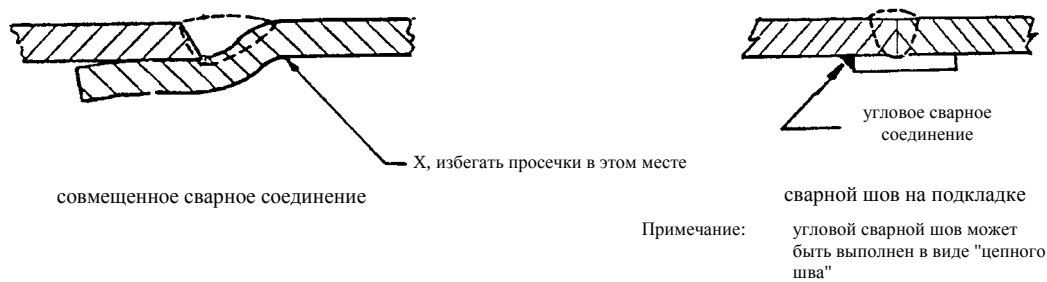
Кольцевое стыковое сварное соединение
